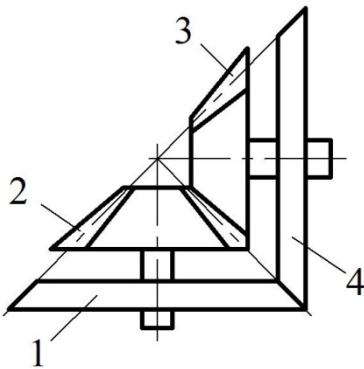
Схема контроля кинематической погрешности конических зубчатых колес
